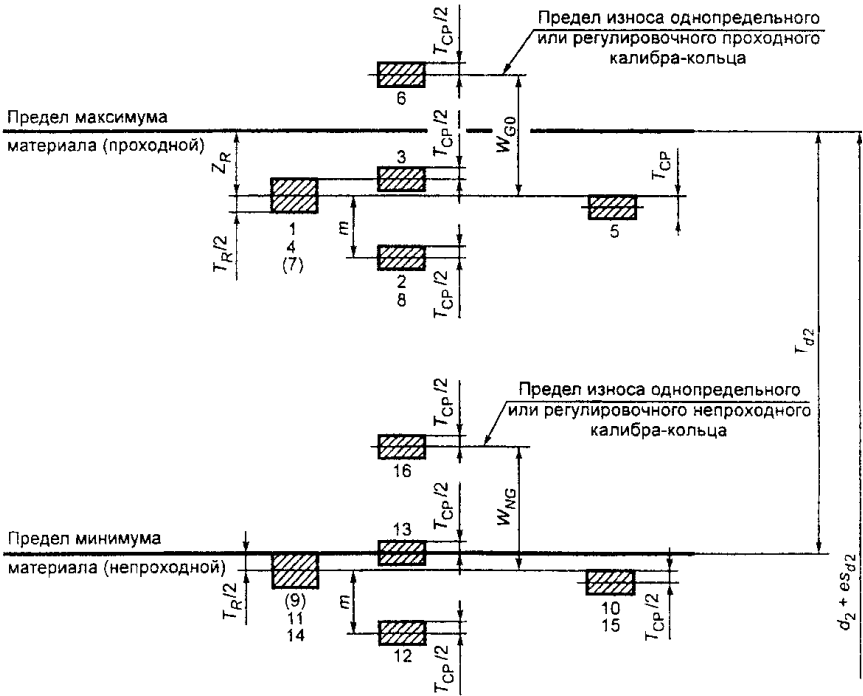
Схемы расположения полей допусков среднего диаметра калибров для контроля резьбы $M36 \times 1-7g6g-14$, мкм
